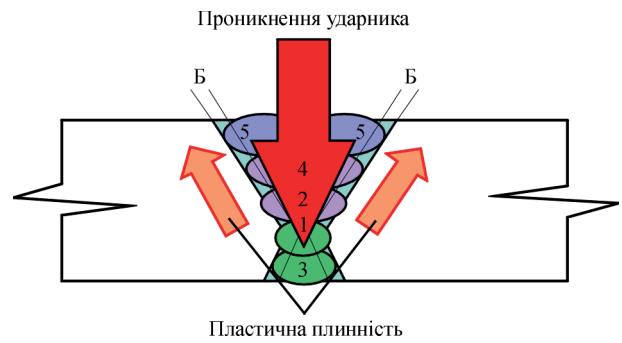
Схематичне зображення взаємодії металу комбінованого зварного шва з високошвидкісним ударником [9]: Б – буферний прошарок, наплавлений на крайки стика; 1–6 – послідовність зварювання шарів шва (1, 3, 5, 6 – аустенітна (нержавка) сталь, 2, 4 – зносостійкий матеріал високої твердості)
